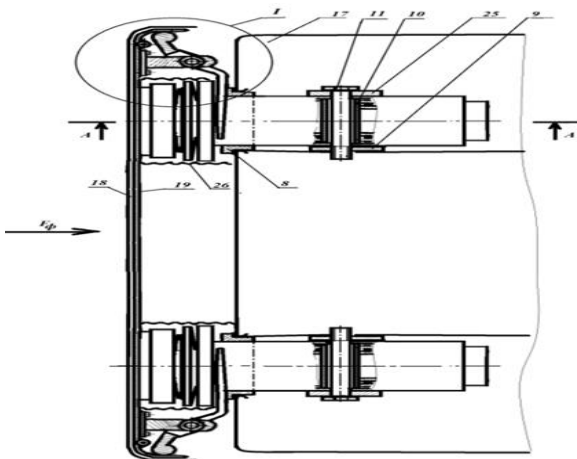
Схема ударозащитного устройства, вид сверху и места
